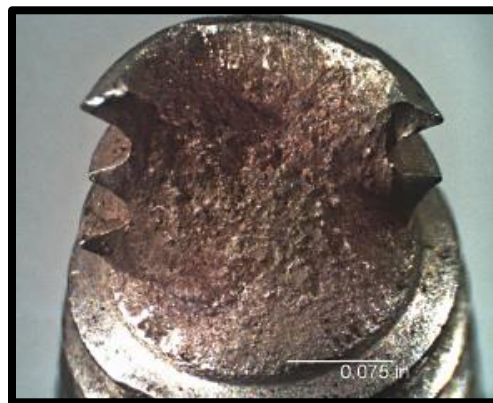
Fractura dúctil a flexión en tornillo [IDDP].
